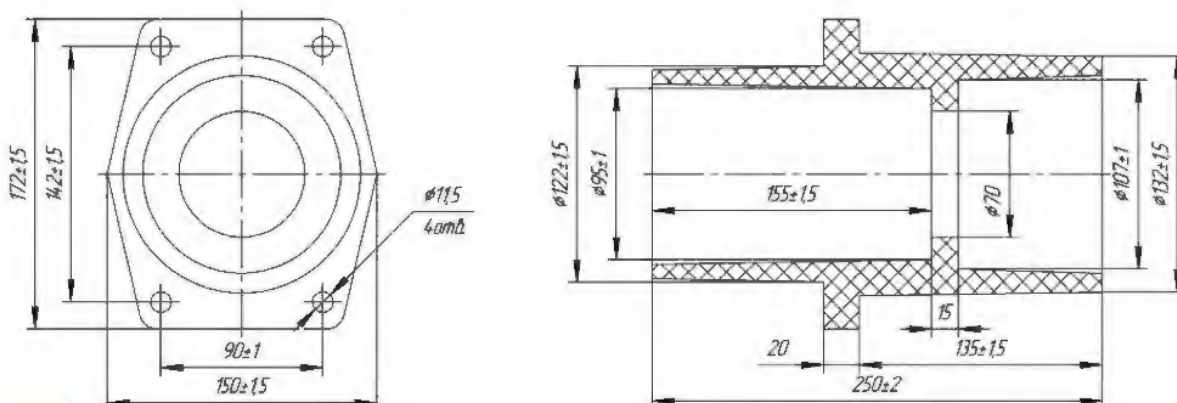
Габаритные и установочные размеры изолятора проходного ИПЛ-10/8 IV.
